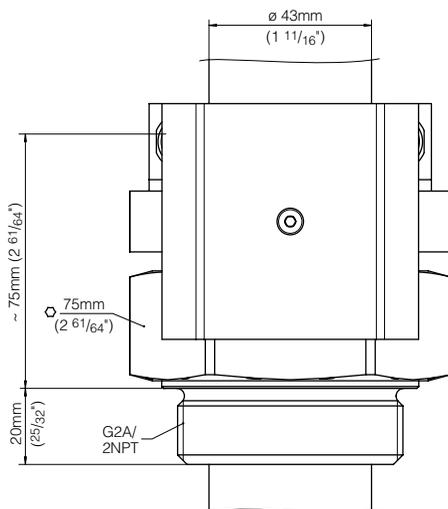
Проходной фитинг ARV 33 до 16 бар для OPTISWITCH 3300 C
